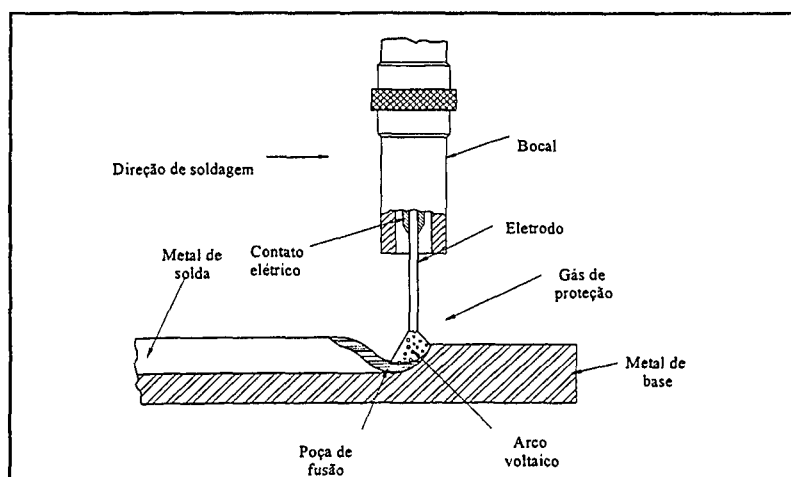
Detalhe da soldagem MIG/MAG (Miranda, 1999).
